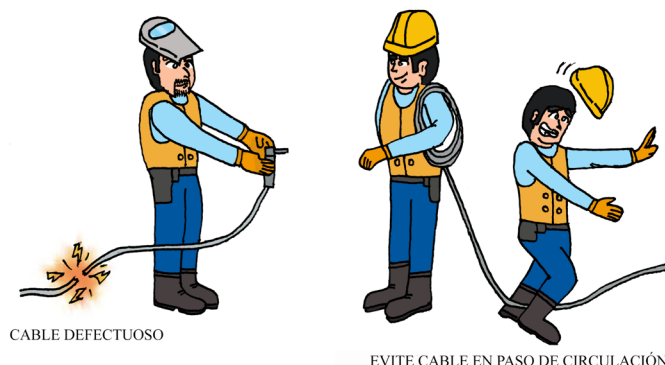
Revisión de cables y conexiones de soldadora
